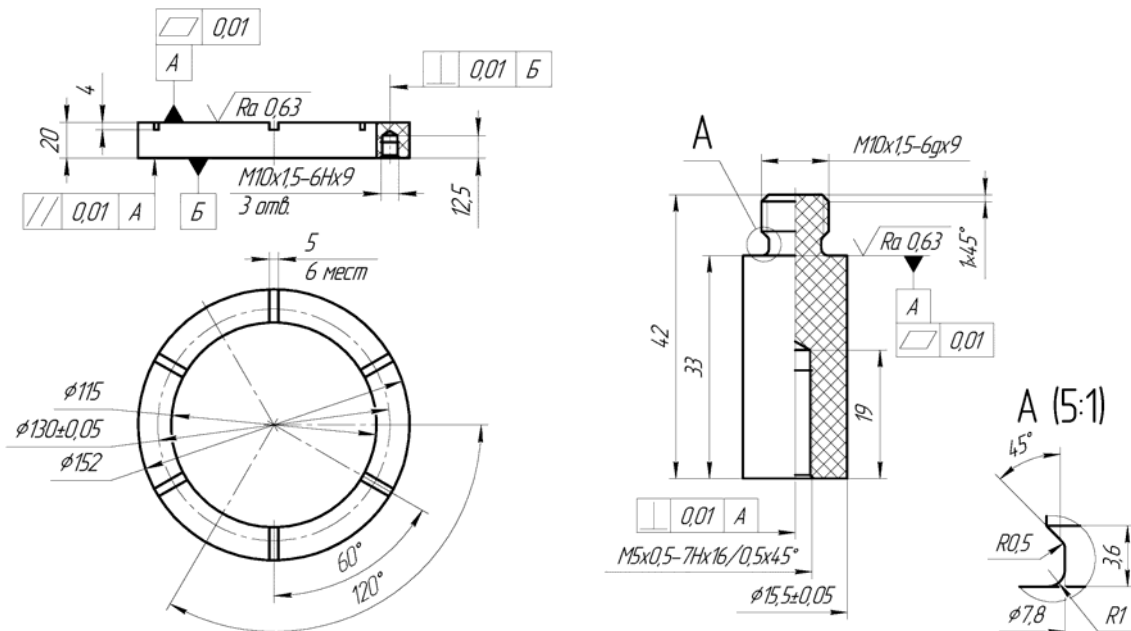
Чертеж опорного кольца прецизионного держателя пластин
